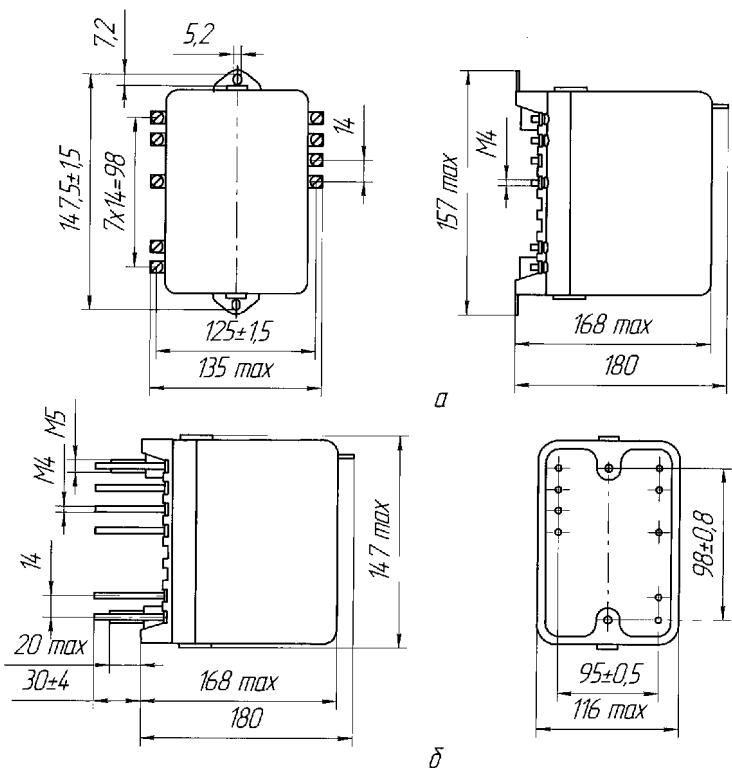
Габаритные, установочные и присоединительные размеры устройства типа УСЗ 2/2.
